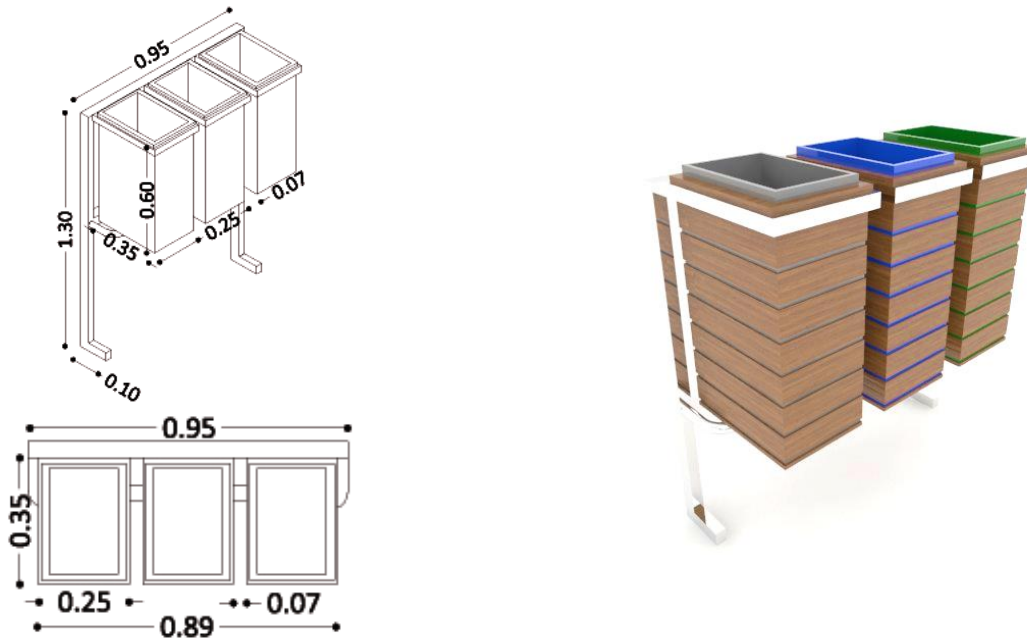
Planimetría y render, punto ecológico. Fuente: grupo de investigación.
